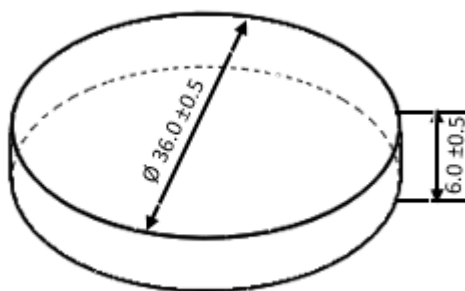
Dimensiones de la probeta para las pruebas de compresión
